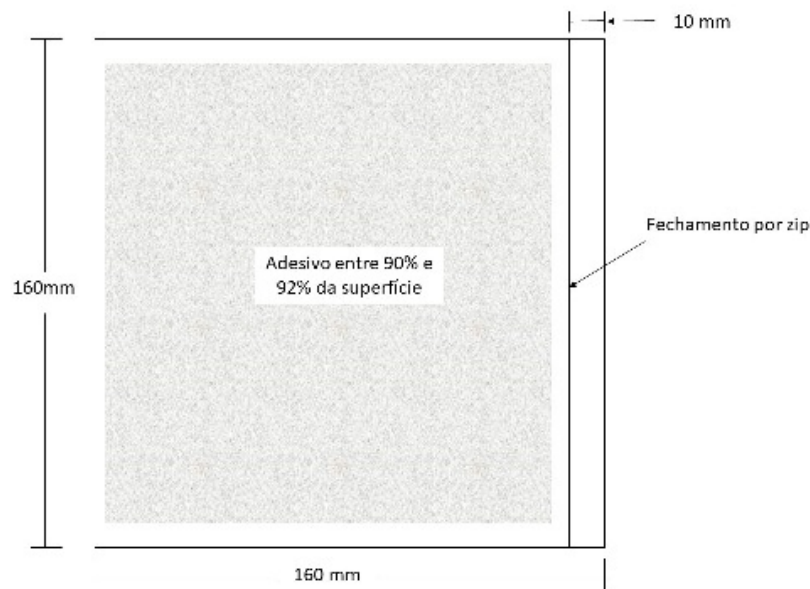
Envelope plástico para embalagem da urna eletrônica
